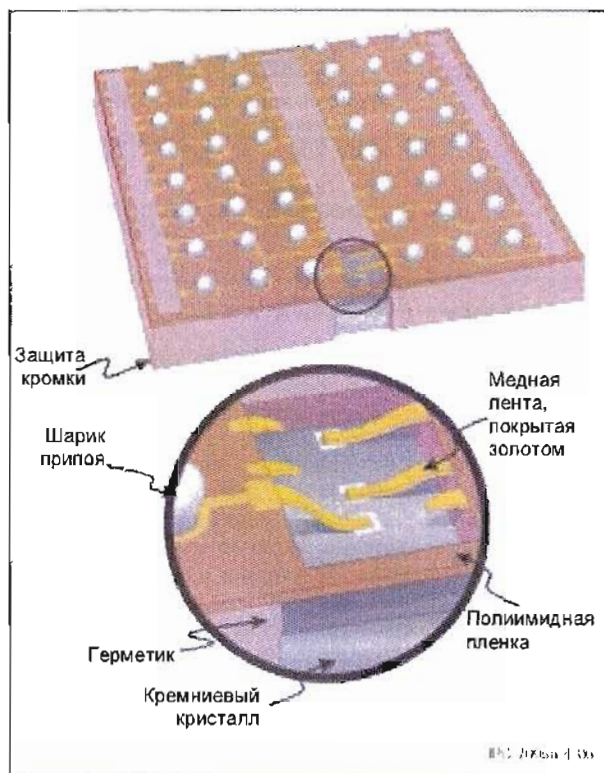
Подложка корпуса мBGA на основе полиимидной пленки с приваренными выводами обеспечивает надежное соединение между контактными площадками кристалла и шариковыми выводами.
